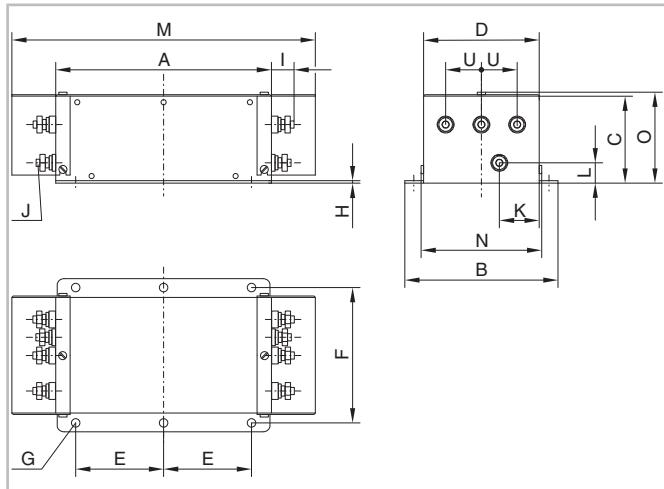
Габаритный чертеж RFI фильтра 3259-250-28
